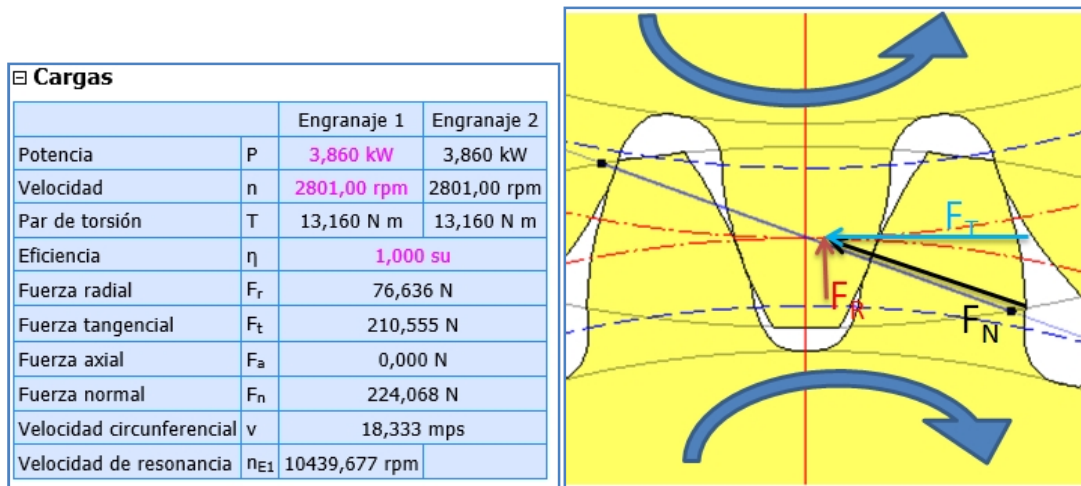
A. Resultado de carga de engranajes para primera hipótesis.- Izquierda. Figura 8.4.B. Interpretación del sentido de las fuerzas del eje superior en función del giro del engranaje.- Derecha.
